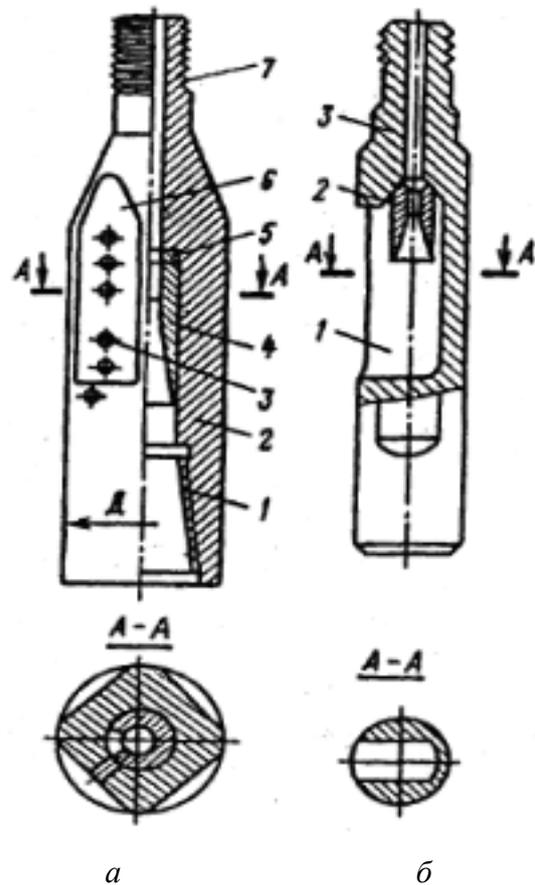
Канатные замки: *a* – с вращающейся втулкой: 1 – резьба; 2 – корпус; 3 – отверстия; 4 – втулка; 5 – шайба; 6 – скос; 7 – кольцевые проточки; *б* – замок с боковым окном: 1 – окно; 2 – втулка; 3 – корпус
